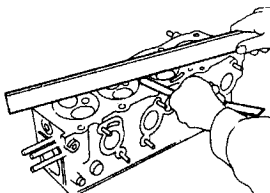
Проверьте поверхность головки блока цилиндров на наличие деформации (См. Раздел 17)
